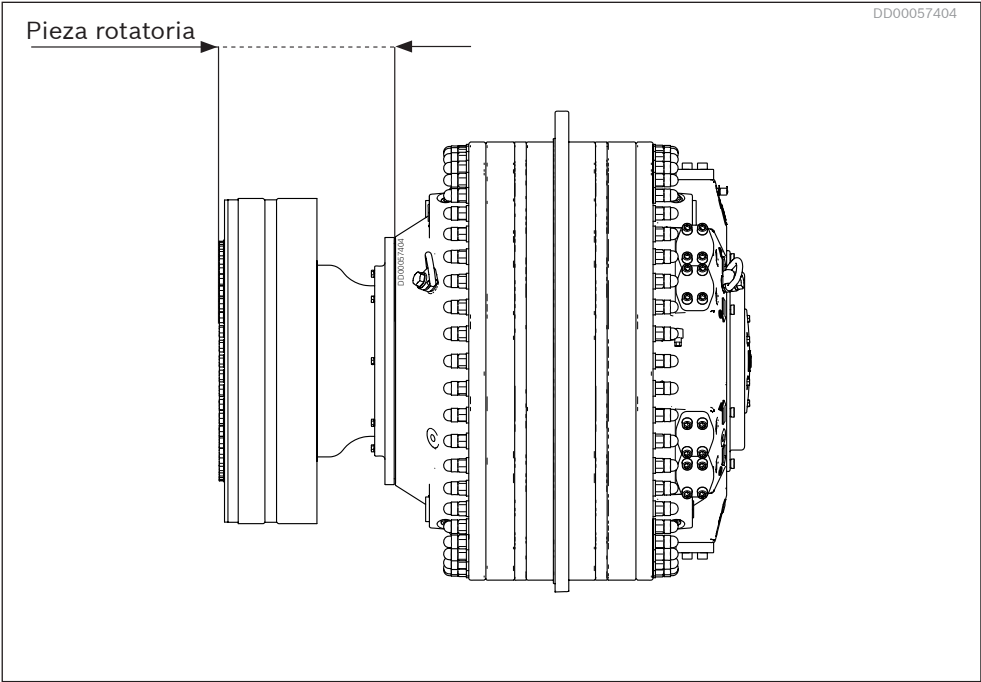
Pieza rotatoria, motor con adaptador de acoplamiento
